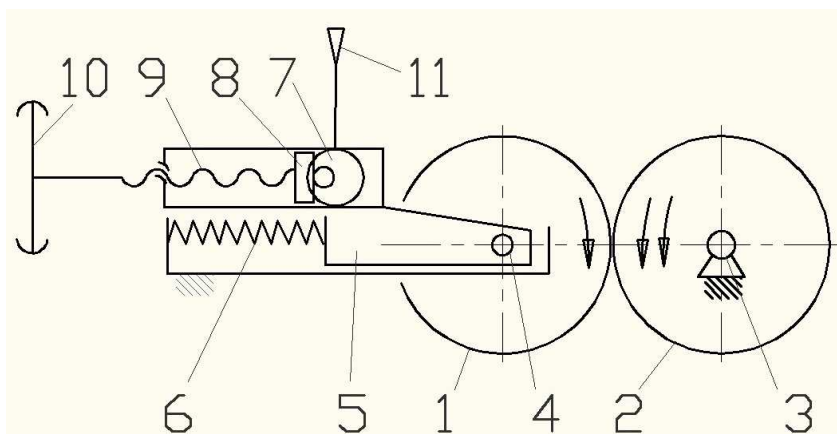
Конструкция установочного механизма с эксцентриковым валом
